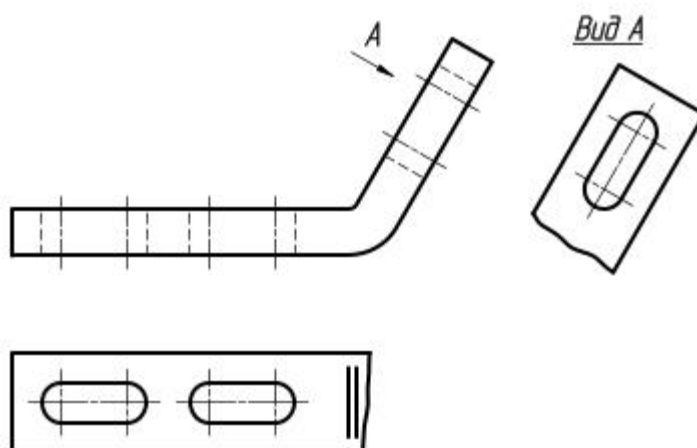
Дополнительный вид со стрелкой и надписью
